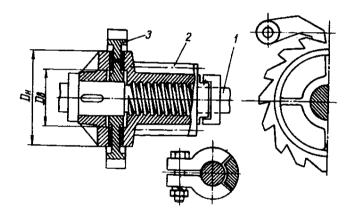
Грузоупорный тормоз: 1 – вал; 2 – шестерня; 3 – храповик
